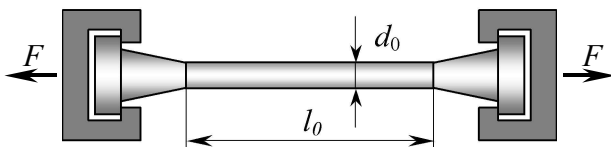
Циліндричний зразок для випробувань на розтяг
